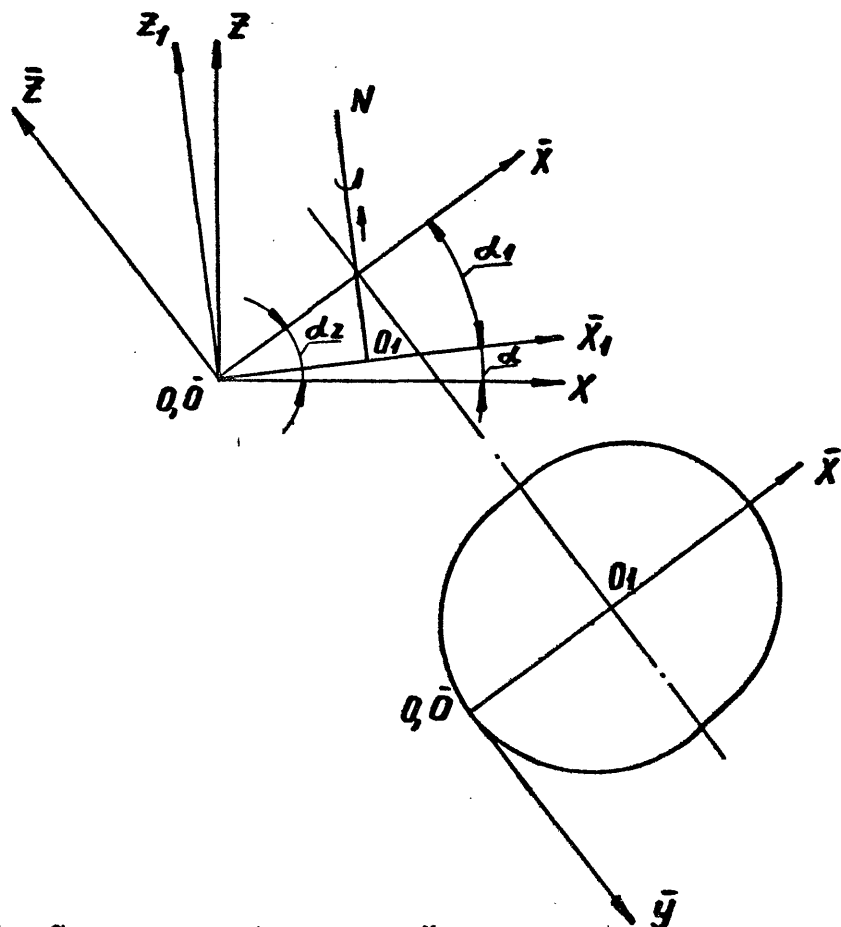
Схема обработки несферических поверхностей /осевое движение суппорта/.
